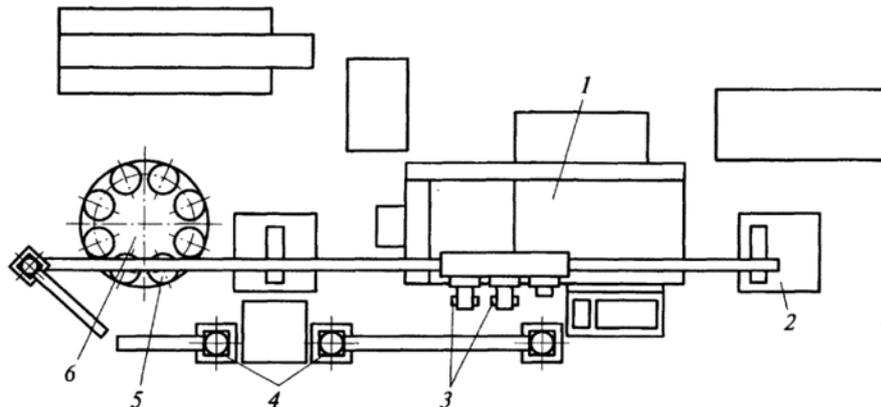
Автоматизований технологічний комплекс для механічної обробки
